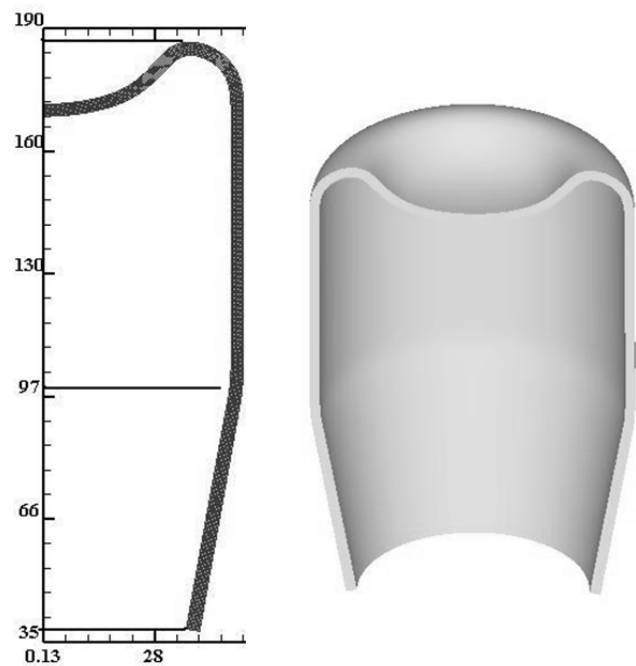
Розміри (мм) половини zdeформованої заготовки та загальний вигляд в розрізі
